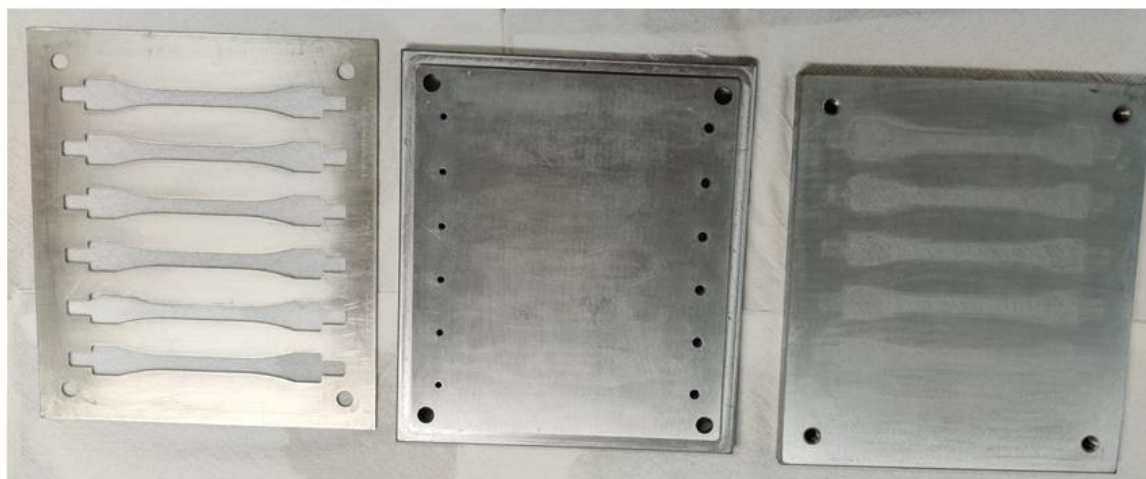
Placas constituintes do molde para fabrico de provetes maciços de adesivo
